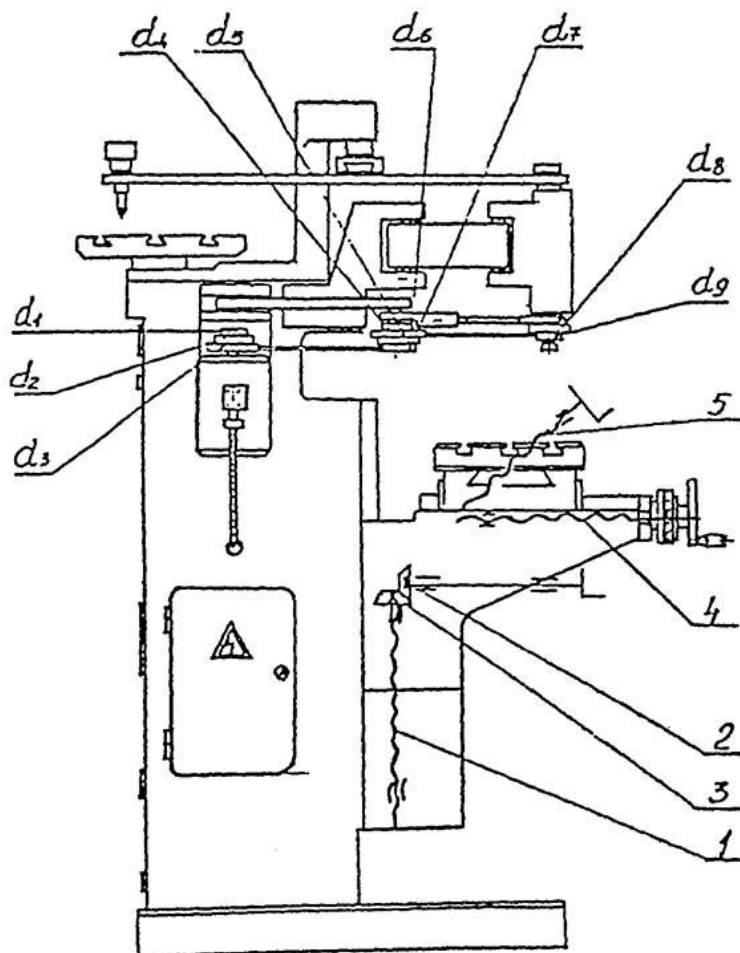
Кінематична схема фрезерного верстату 6Е463
